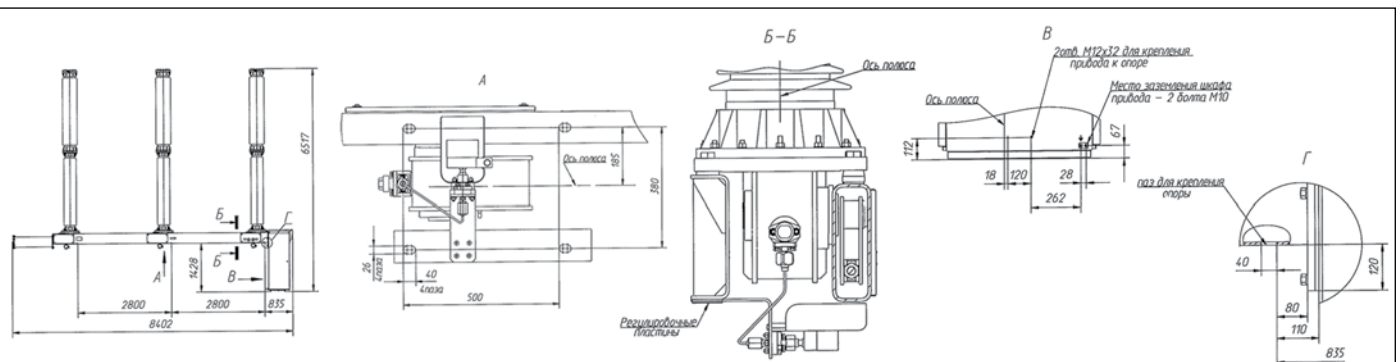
Габаритные и установочные размеры выключателя ВГТ-УЭТМ®- 1А1-220 в исполнении без опорных металлоконструкций. Неуказанные размеры см. на рис. 1.
